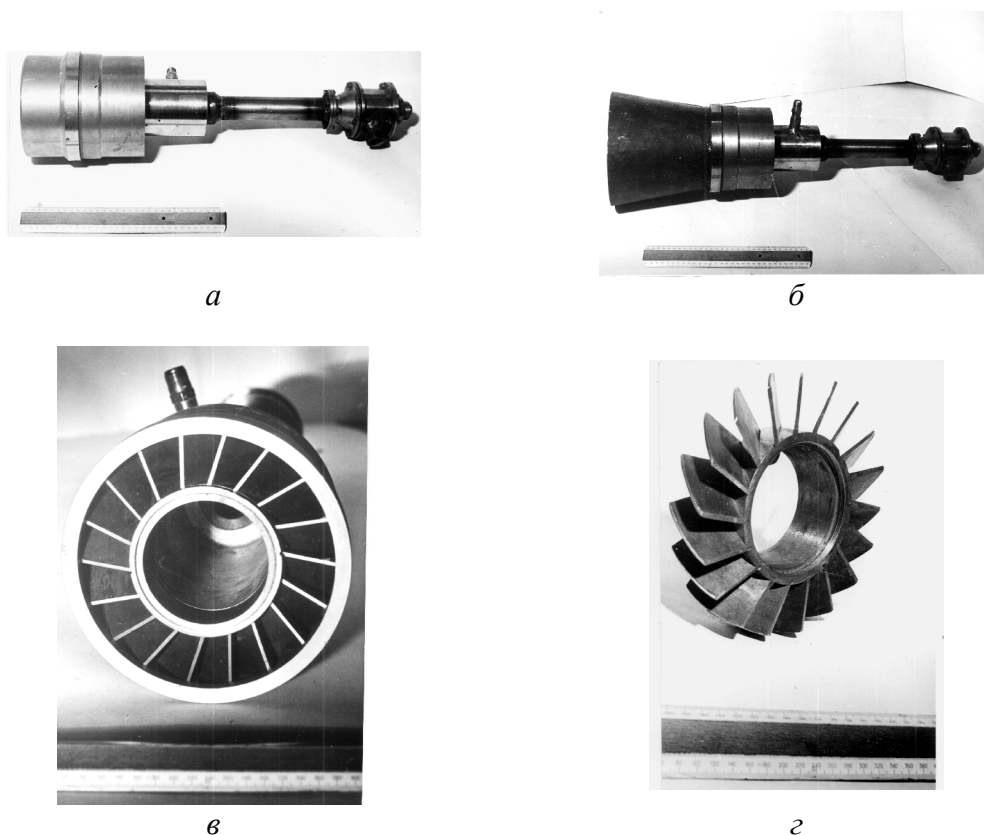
Общий вид горелочных устройств: а - горелка с цилиндрической насадкой; б - с диффузорной насадкой; в - вид со стороны среза камеры; г - конструкция завихрительного устройства с прямыми лопатками ($\alpha = 45^\circ$)
